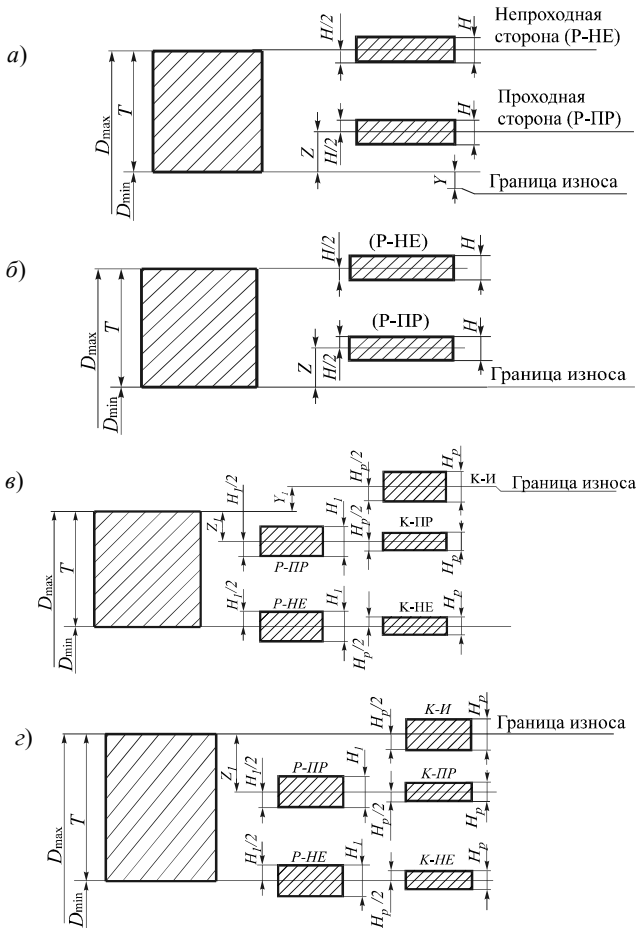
Схемы расположения полей допусков калибров для номинальных размеров до 180 мм по ГОСТ 24853 для контроля:
